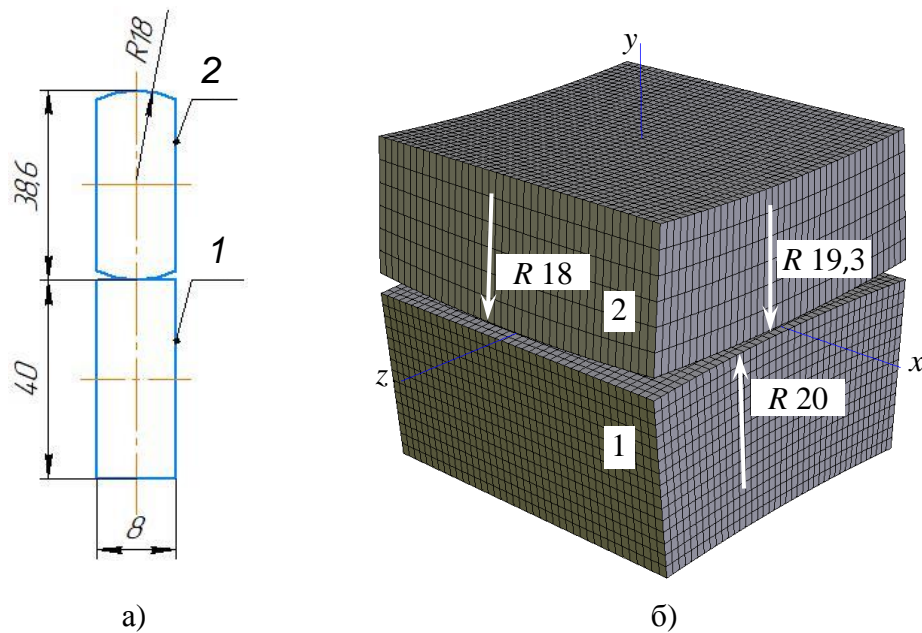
Образец цилиндрической формы из колёсной стали (1) и контролик тороидальной формы (2): а – схема испытаний; б – конечноэлементные модели
